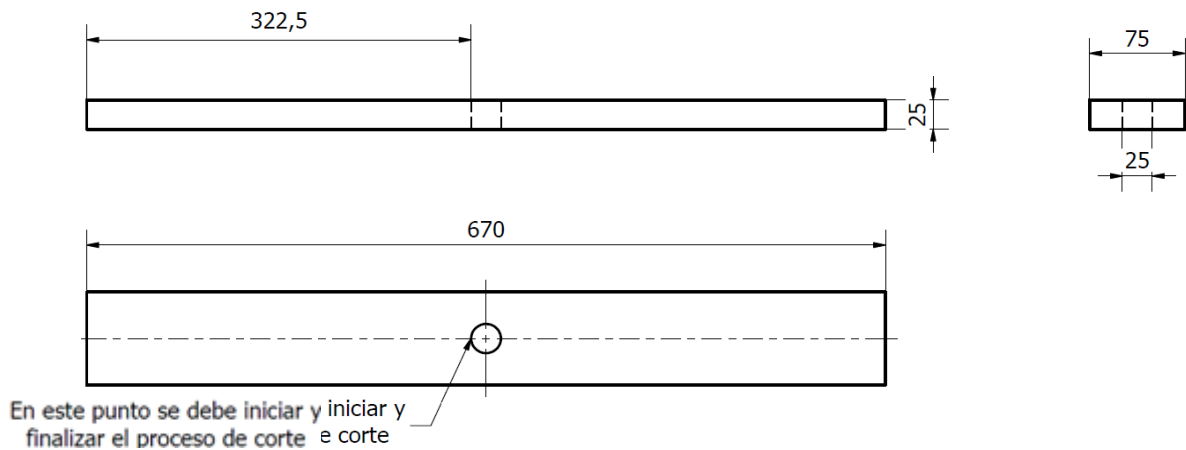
Geometría de la probeta con agujero y espesor 25 mm. Dimensiones en mm.
